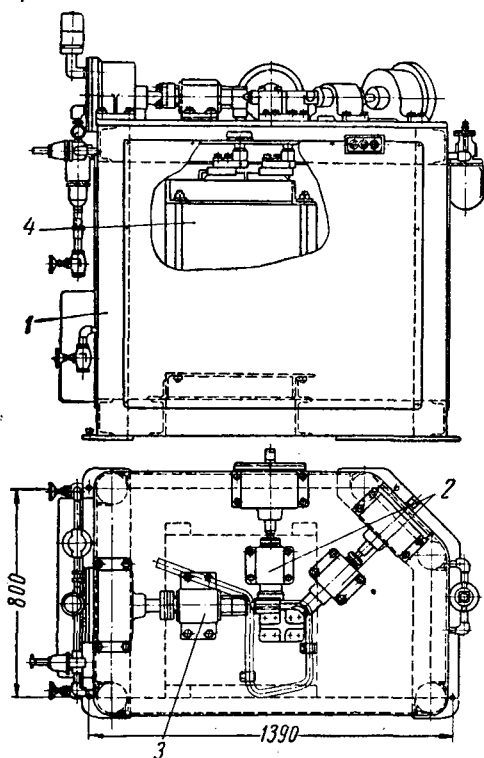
Общий вид конденсаторной машины для сварки соединения основания остова.
